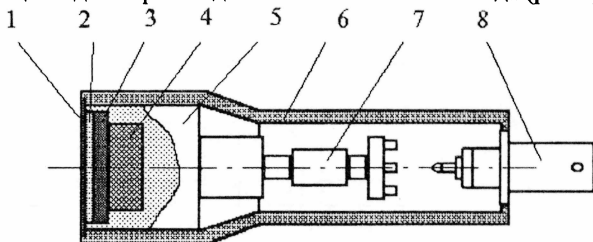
Конструкция ультразвукового зонда для одномерной эхо - энцефалографии: 1 - второй согласующий слой; 2 - первый согласующий слой; 3 - пьезокерамическая пластина; 4 - демпфер; 5 - втулка акустической развязки; 6 - металлический корпус; 7 - согласующий трансформатор; 8 - высокочастотный разъем
